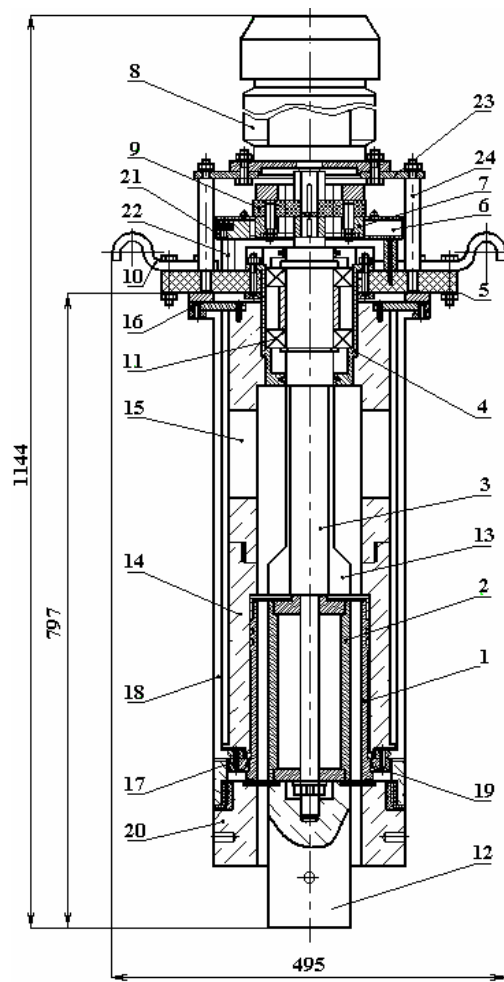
Промышленная установка: 1 – цилиндр; 2 – анод; 3 – вал; 4 – корпус; 5 – несущая траверса; 6 – графитовая щетка; 7 – коллектор; 8 – электродвигатель; 9 – муфта; 10 – токоподвод; 11 – подшипник; 12 – цилиндрическая гайка; 13 – трубка; 14 – обойма; 15 – окна; 16 – верхний кольцевой токоподвод; 17 – нижний кольцевой токоподвод; 18 – латунная штанга; 19 – медная цанга; 20 – кольцевая гайка; 21 – щеткодержатель; 22 – текстолитовая ножка; 23 – металлическая плита; 24 – стойка
